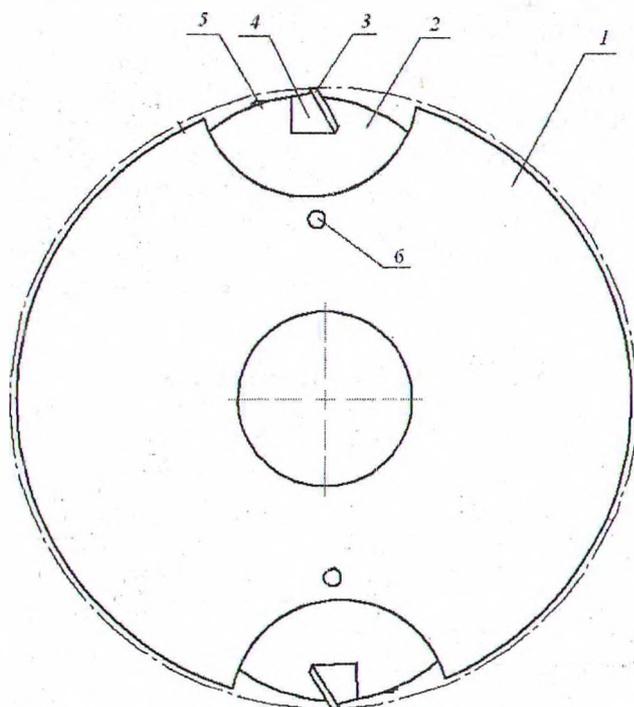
Сборная фреза с изменяемыми углами резания: 1 – корпус фрезы; 2 – сегменты-ножедержатели; 3 – нож; 4 – клин; 5 – винт крепления ножа; 6 – винт крепления сегмента
